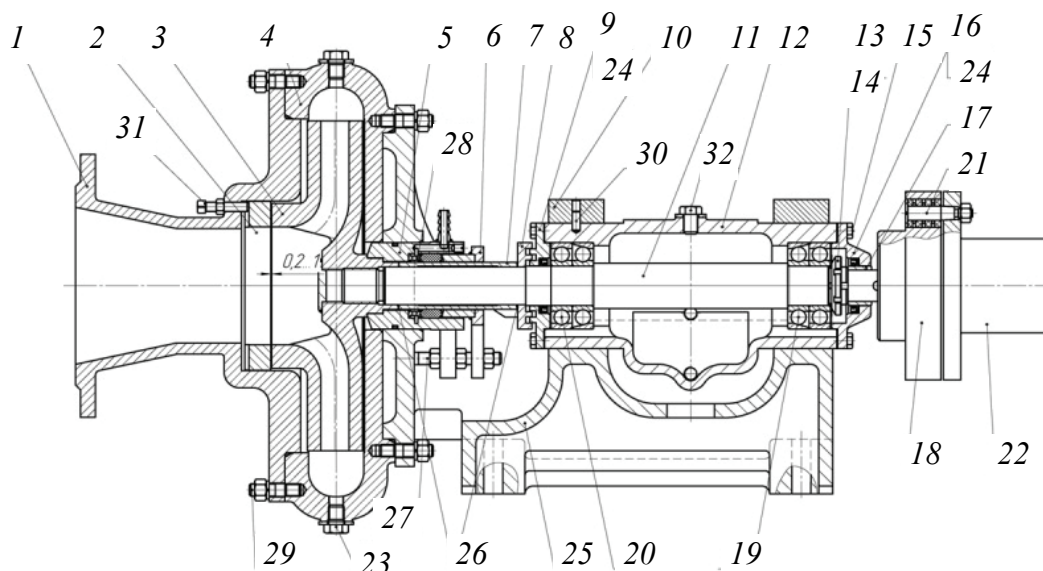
Общий вид шламового насоса 6Ш8 (6Ш8-2): 1 – всасывающий патрубок; 2 – кольцо уплотнительное; 3 – колесо рабочее; 4 – корпус спиральный; 5 – корпус уплотнения; 6 – корпус сальника; 7 – втулка (подсальниковая); 8 – кольцо лабиринтное; 9 – крышка подшипника передняя; 10 – скоба; 11 – вал; 12 – корпус подшипника; 13 – гайка; 14 – шайба; 15 – болты; 16 – крышка подшипниковая задняя; 17 – втулка; 18 – полумуфта шламового насоса; 19 – подшипник 346310; 20 – подшипник 310; 21 – пальцы муфты; 22 – полумуфта электродвигателя; 23 – пробка; 24 – манжета 1.2–50×70; 25 – корпус шламового насоса; 26 – кольцо регулировочное; 27 – шпилька М16×125; 28 – кольцо сальника; 29 – шпилька М16×125; 30 – штифт; 31 – винт регулировочный М12×55; 32 – пробка подшипниковая
